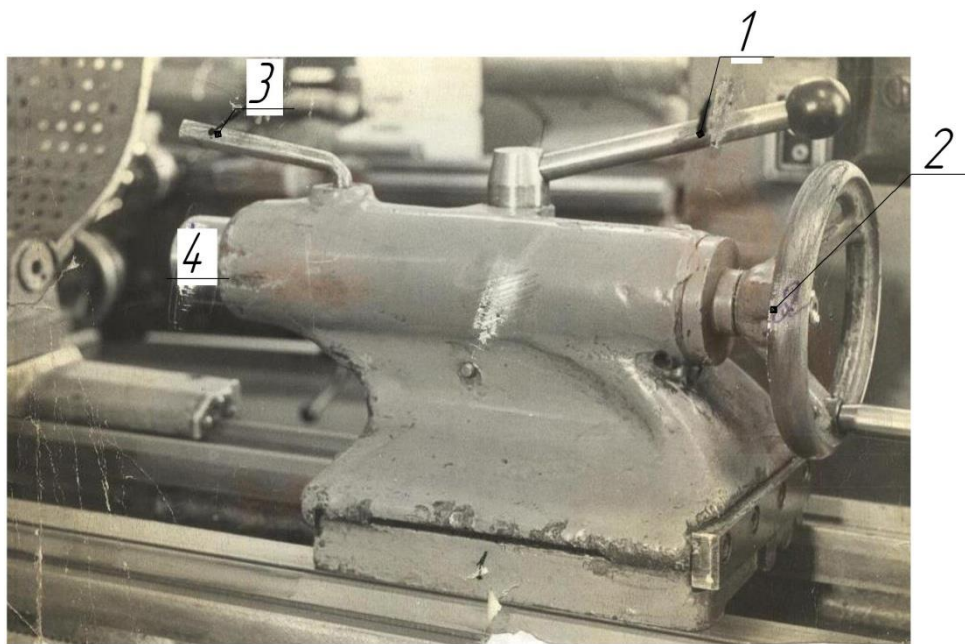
Задняя бабка: 1 – рукоятка, фиксирующая положение задней бабки на станине; 2 – маховик для осевого перемещения пиноли; 3 – рукоятка фиксирующая положение пиноли; 4 – пиноль
